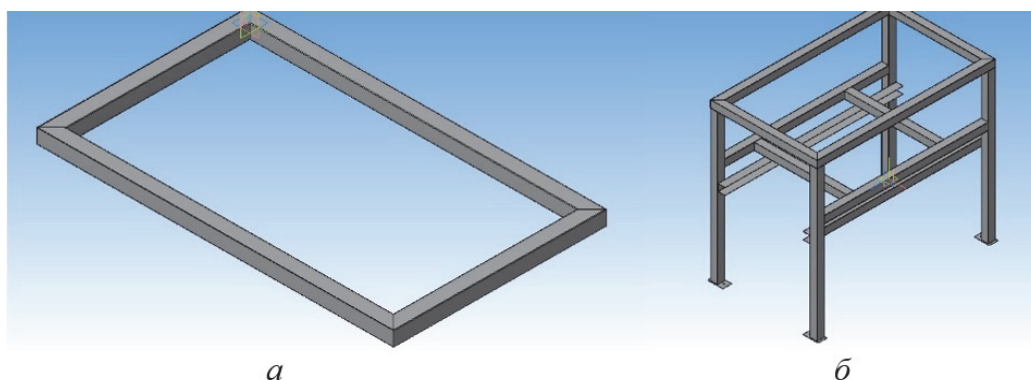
Рама для крепления опорной конструкции и бортов: а – отдельно; б – в конструкции
